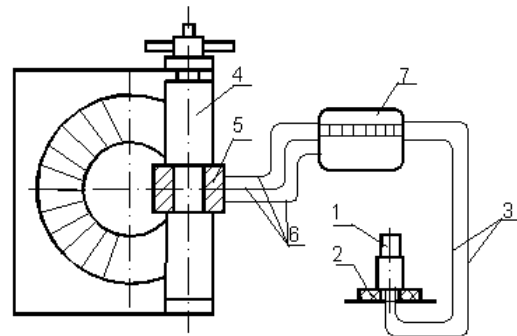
Схема сборки деталей соединений со встроенными термопарами
